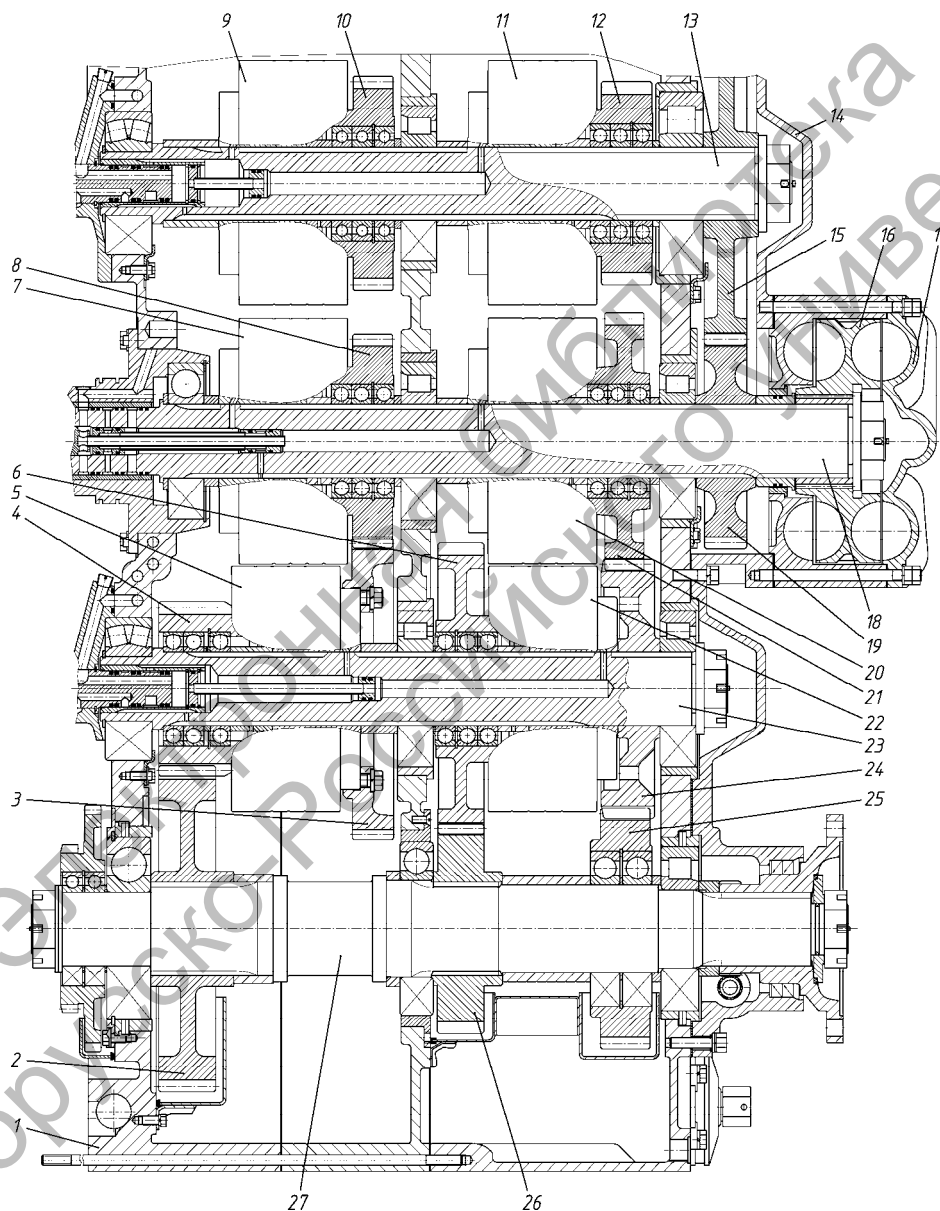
Коробка передач карьерного самосвала БелАЗ-7555Е
